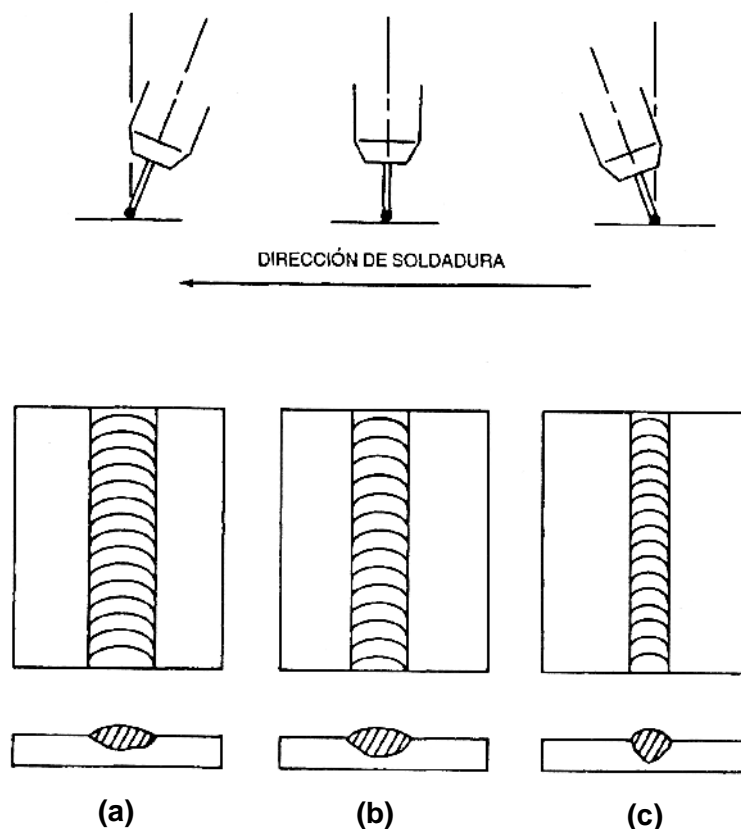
Efecto de la posición del electrodo y de la técnica de soldadura: (a) Técnica de derecha, (b) Soplete perpendicular y (c) Técnica de revés (23)
